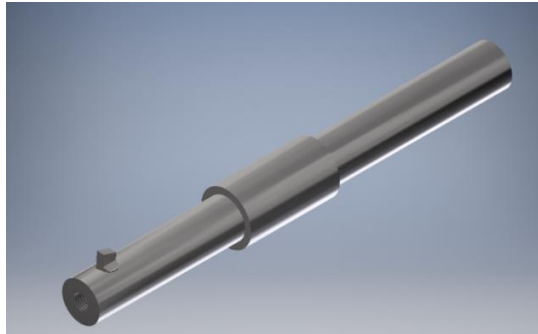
Diseño preliminar de portaherramienta ensamblado con herramienta.
